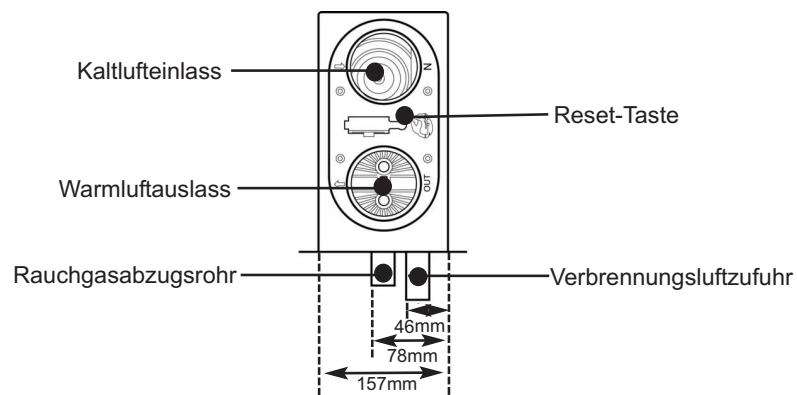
Interne Montage - Frontansicht - SH2201 oder SC2201
